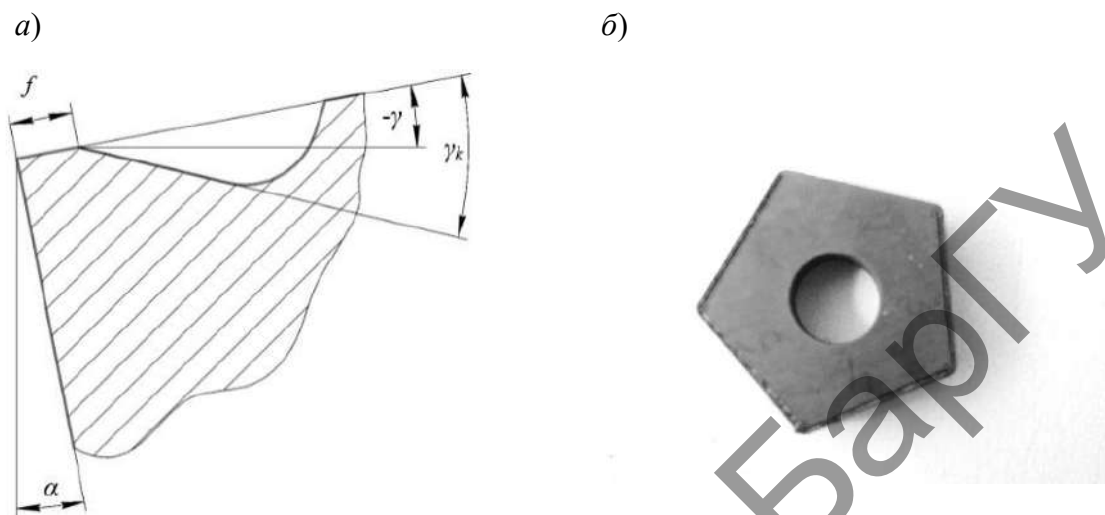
Схема канавки (а) и внешний вид пластины с канавками (б)
